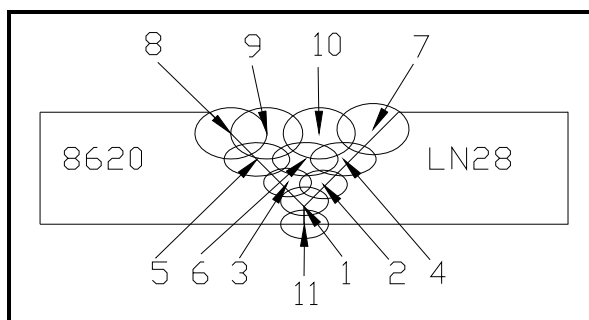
Seqüência de passes utilizada no processo de soldagem dos corpos de prova.
